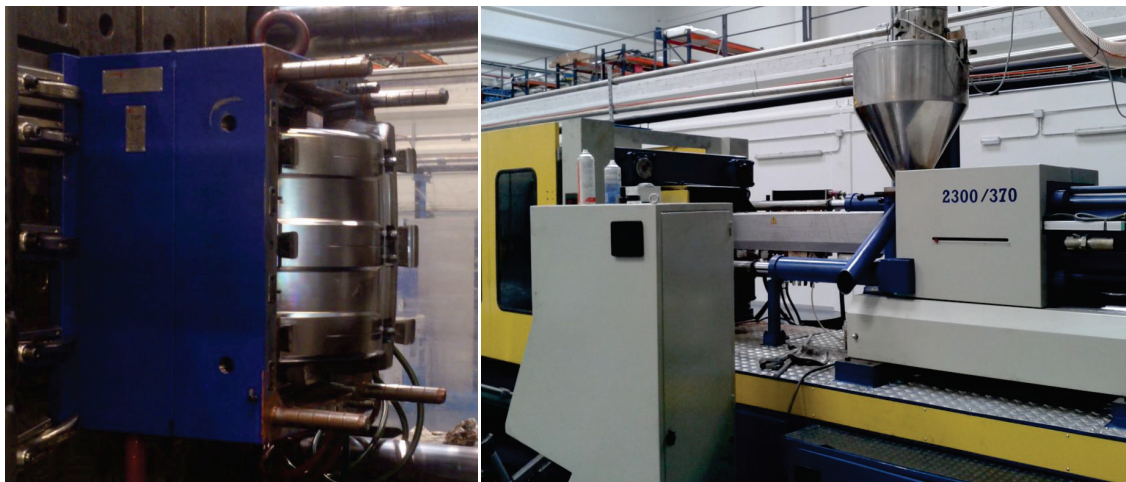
MOLDE Y MÁQUINA DE INYECCIÓN
